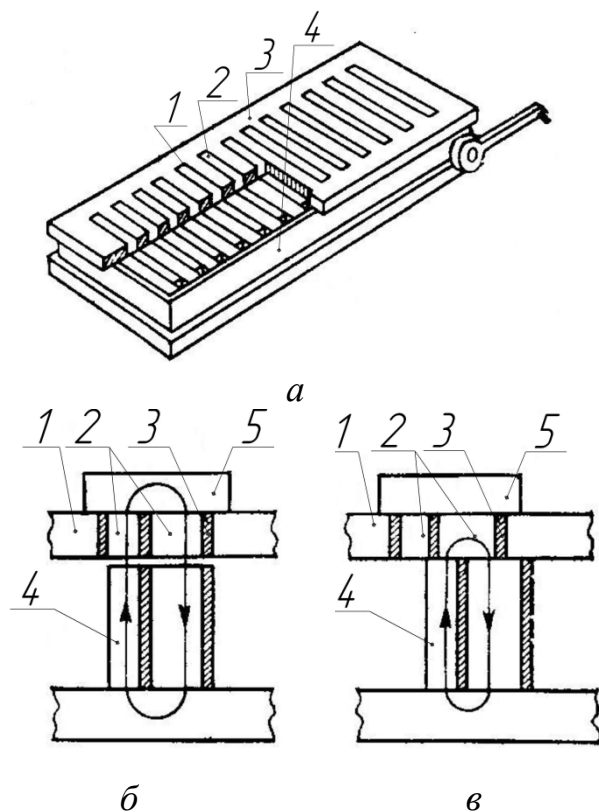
Магнитная плита: а — общий вид; в — положение магнитов и действие магнитного потока при закреплении заготовки; в — положение магнитов и действие магнитного потока при установке и снятии заготовки; 1, 2 — железные пластины; 3 — немагнитные прослойки между пластинами; 4 — магниты; 5 — заготовка
